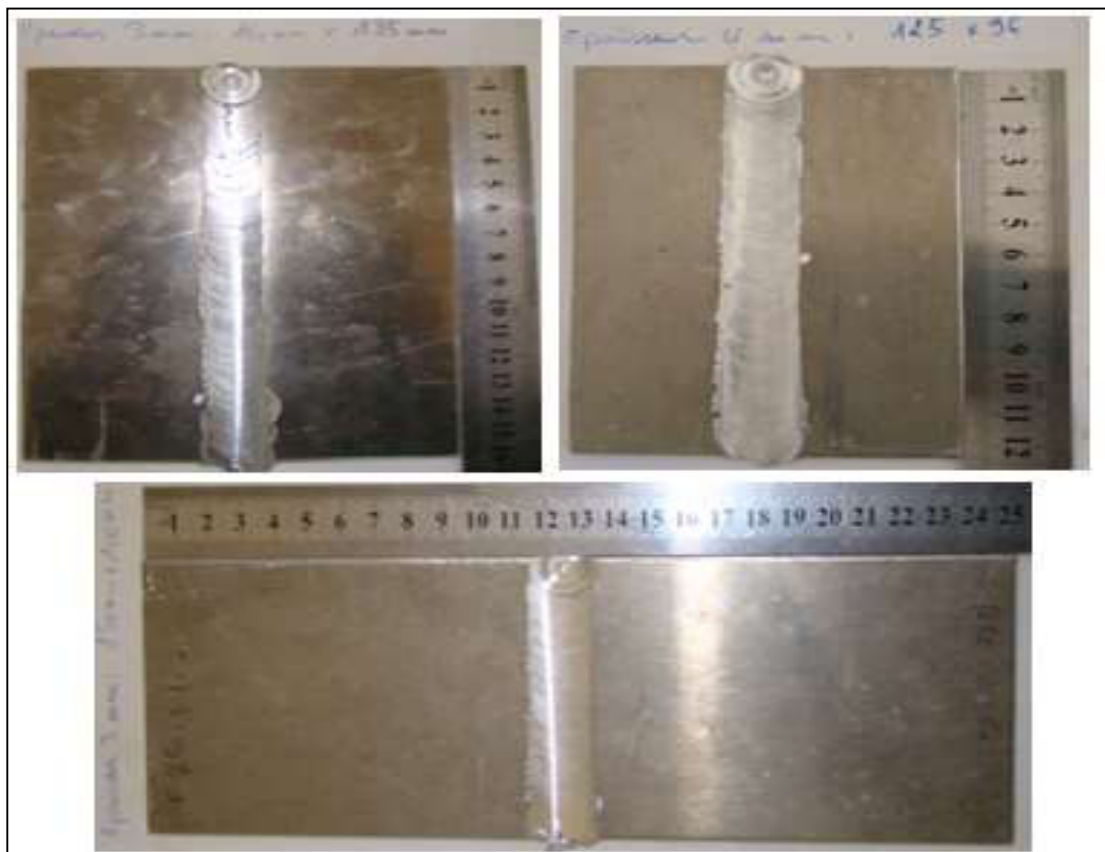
Plaques soudées par le procédé FSW
